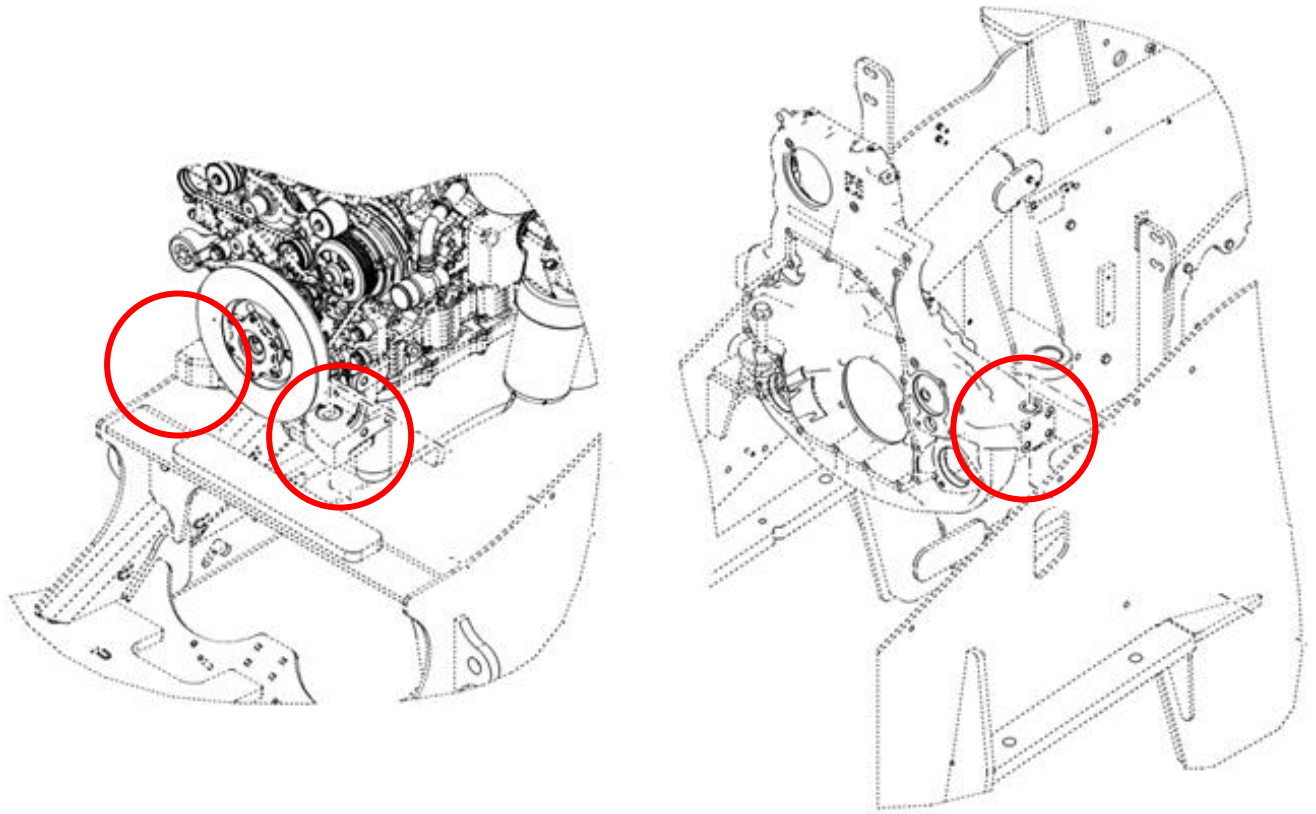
Схема с внешним видом крепления установки опор двигателя FPT
